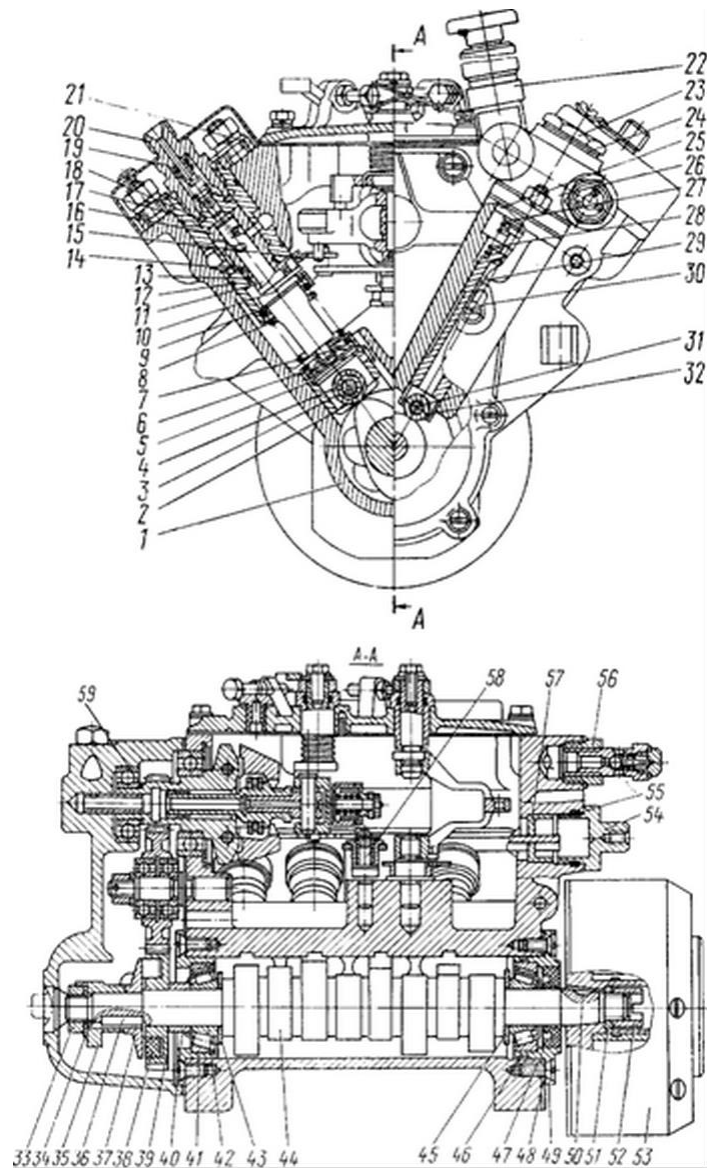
Топливный насос высокого давления: 1 – корпус; 2, 32 – ролики толкателей; 3, 31 – оси роликов; 4 - втулка ролика; 5 – пята толкателя; 6 – сухарь; 7 – тарелка пружины толкателя; 8 – пружина толкателя; 9, 34, 43, 45, 51 – шайбы; 10 – втулка поворотная; 11 – плунжер; 12, 13, 46, 55 – кольца уплотнительные; 14 – штифт установочный; 15 – рейка; 16 – втулка плунжера; 17 – корпус секции; 18 – прокладка нагнетательного клапана; 19 – клапан нагнетательный; 20 – штуцер; 21 – фланец корпуса секции; 22 – насос ручной топливоподкачивающий; 23 – пробка пружины; 24, 48 – прокладки; 25 – корпус насоса низкого давления; 26 – насос топливоподкачивающий низкого давления; 27 – втулка штока; 28 – пружина толкателя; 29 – толкатель; 30 – винт стопорный; 33, 52 – гайки; 35 – эксцентрик привода насоса низкого давления; 36, 50 – шпонки; 37 – фланец ведущей шестерни регулятора; 38 – сухарь ведущей шестерни регулятора; 39 – шестерня ведущая регулятора; 40 – втулка упорная; 41, 49 – крышки подшипника; 42 – подшипник; 44 – вал кулачковый; 47 – манжета с пружиной в сборе; 53 – муфта опережения впрыскивания топлива; 54 – пробка рейки; 56 – клапан перепускной; 57 – втулка рейки; 58 – ось рычага реек; 59 – прокладки регулировочные
